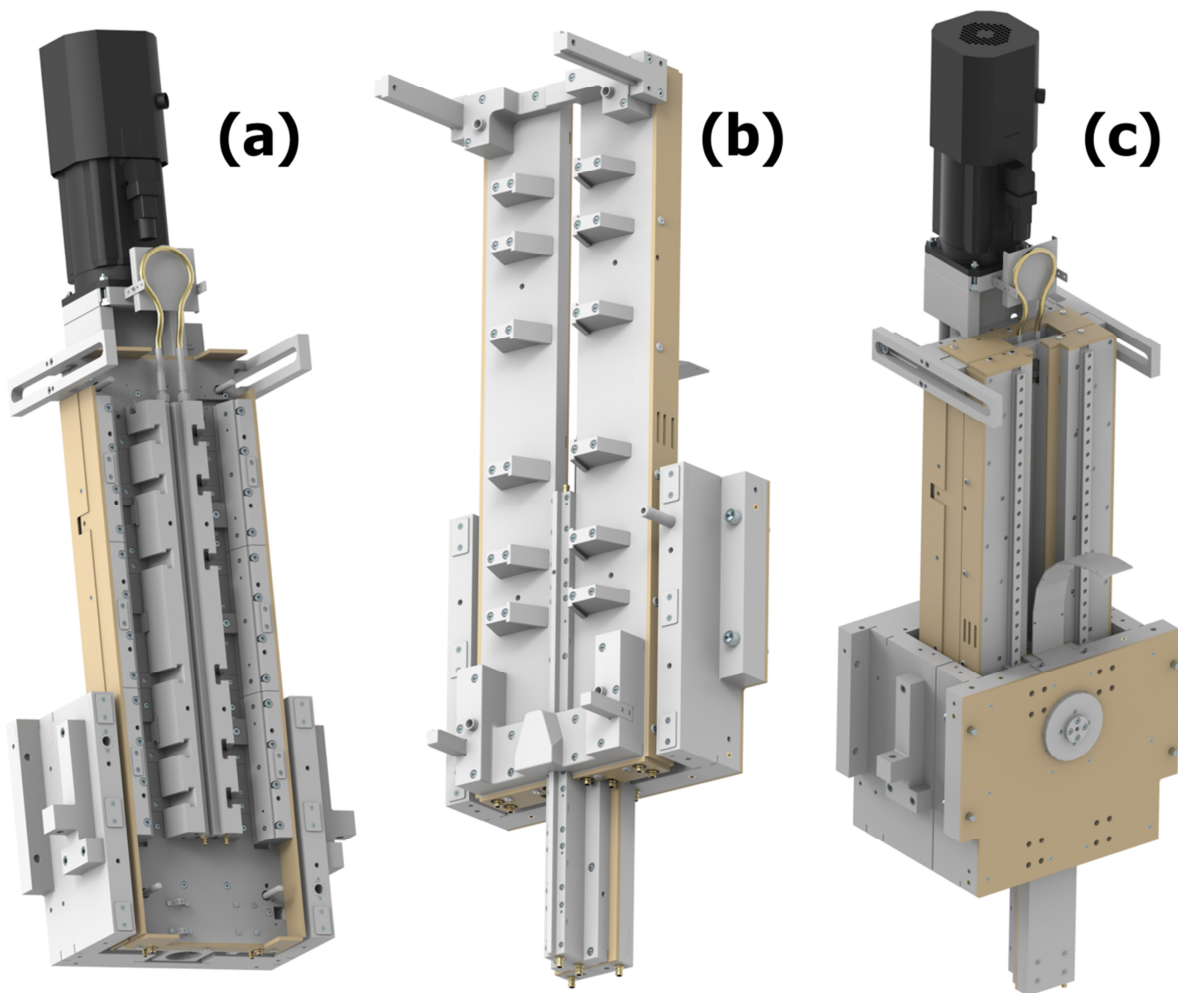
RubExject-Werkzeug (a) Auswerferseitige Werkzeughälfte, (b) düsenseitige Werkzeughälfte, (c) düsenseitige Ansicht auf das gesamte geschlossene Werkzeug [52].
